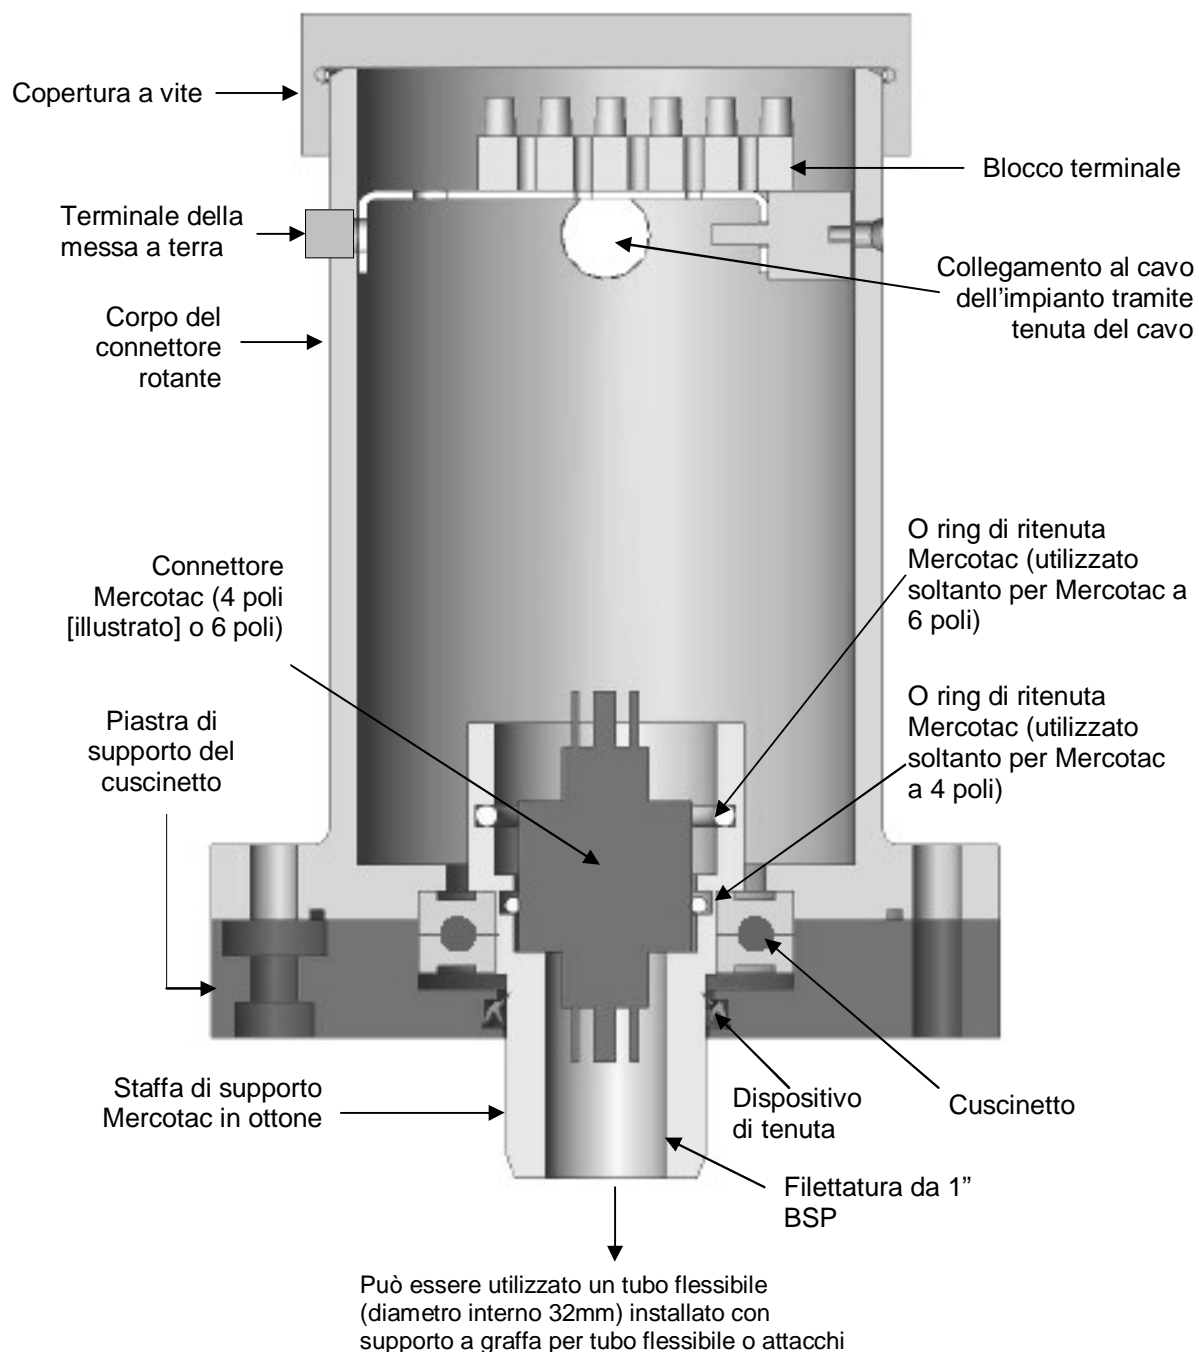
Tipo 'B' assemblaggio del connettore rotante
